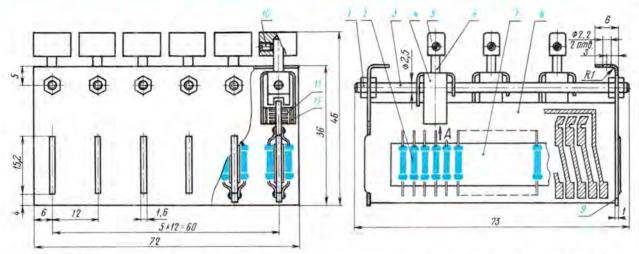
Устройство блока переменных резисторов: 1 — гайка M2,5, 24 шт.; 2 — резистор МЛТ-0,125, 204 шт.; 3 — шпилька-направляющая, Ст. 4X13 («серебрянка»), 6 шт.; 4 — каретка, 6 шт.; 5 — ручка управления, Д16-Т, 6 шт., полировать; 6 — шпилька, 6 шт.; 7 — прокладка, лента изоляционная поливинилхлоридная, 12 шт.; 8 — плата печатная, 6 шт.; 9 — стенка, АМц-П, 2 шт.; 10 — винт установочный М2×4, 6 шт.; 11 — контакт, 12 шт., прикленть эпоксидным клеем к дет, 12; 12 — прокладка, 12 шт., приклеить эпоксидным клеем к лет. 4
